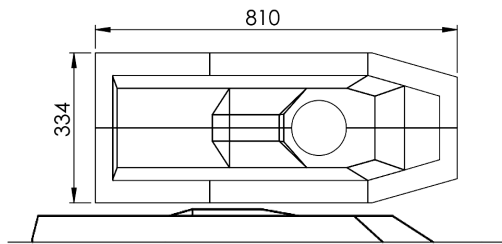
Ескізи креслення макету верхньої проекції корпусу БТР-80
